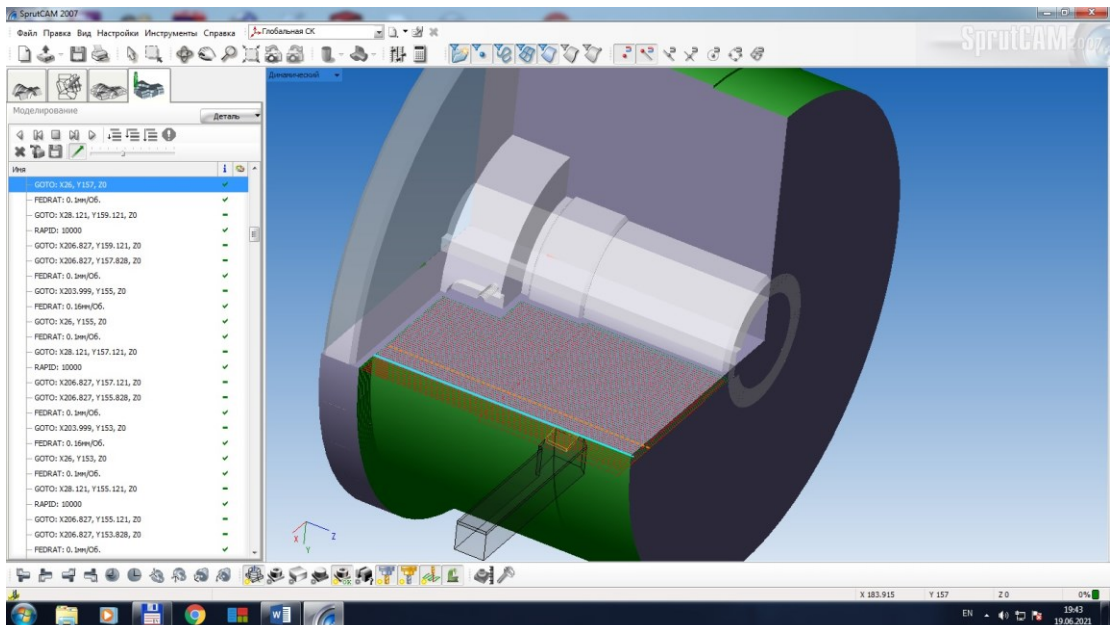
Заготовка з оброблюваною поверхнею та різець
